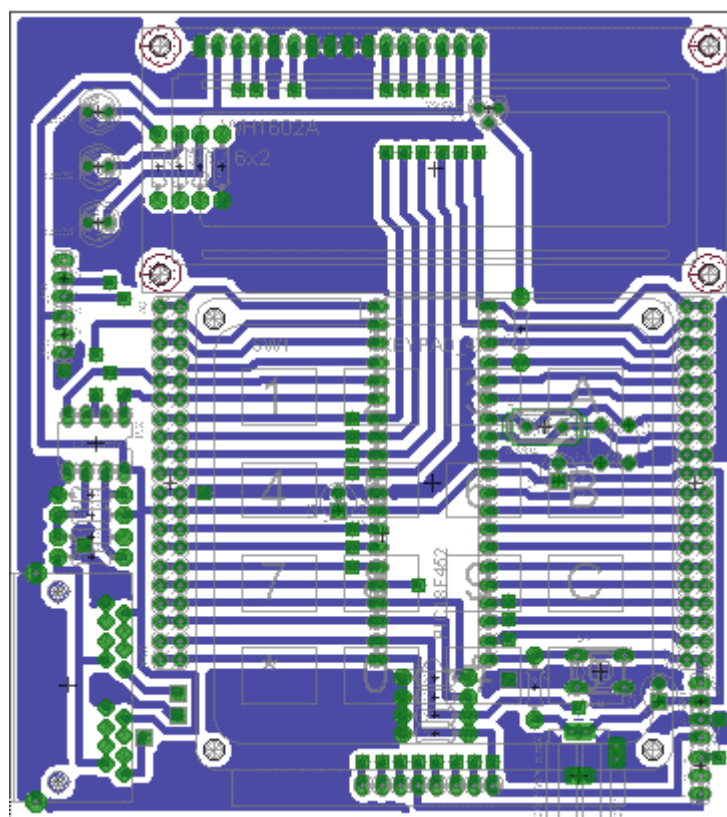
Návrh PCB řídicí jednotky – strana součástek
